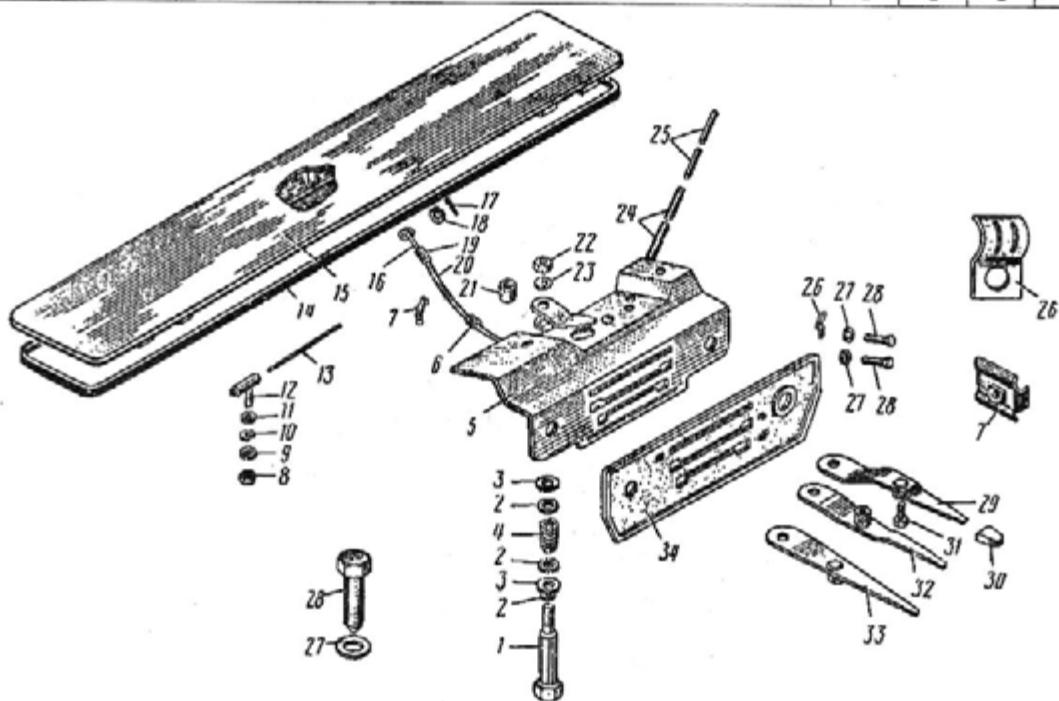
Крышки вентиляционных люков передка кузова и рычаги управления ими
